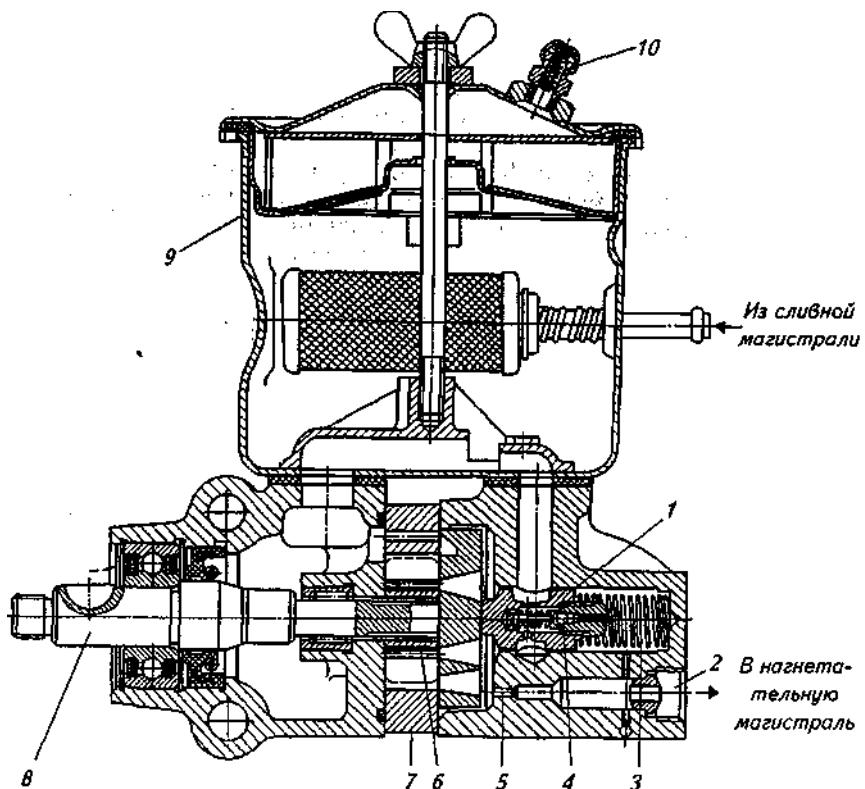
Пластинчатый насос гидроусилителя рулевого управления: 1 — клапан расхода; 2 — корпус; 3 — уравновешивающая пружина; 4 — предохранительный клапан; 5 — жиклер; 6 — ротор; 7 — статор; 8 — приводной вал; 9 — бачок; 10 — сапун.
